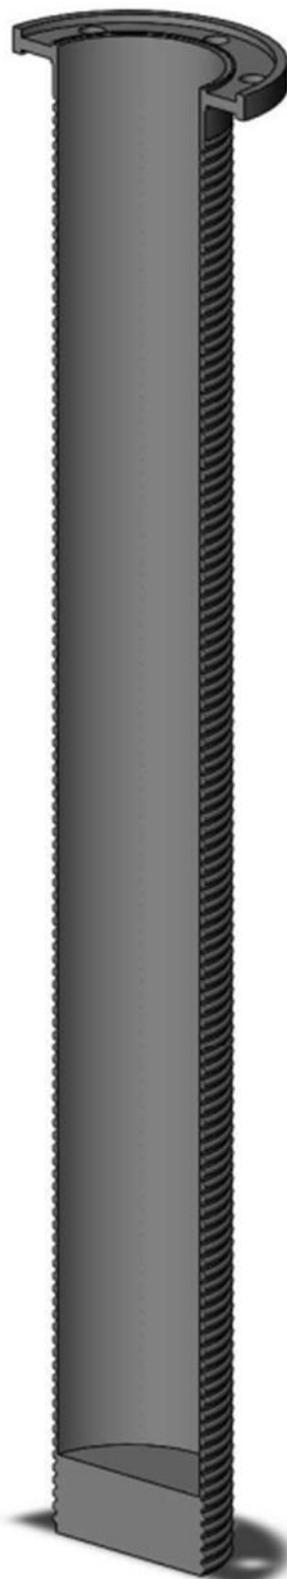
Внешняя полимерная оболочка корпуса магнитоэологического демпфера
